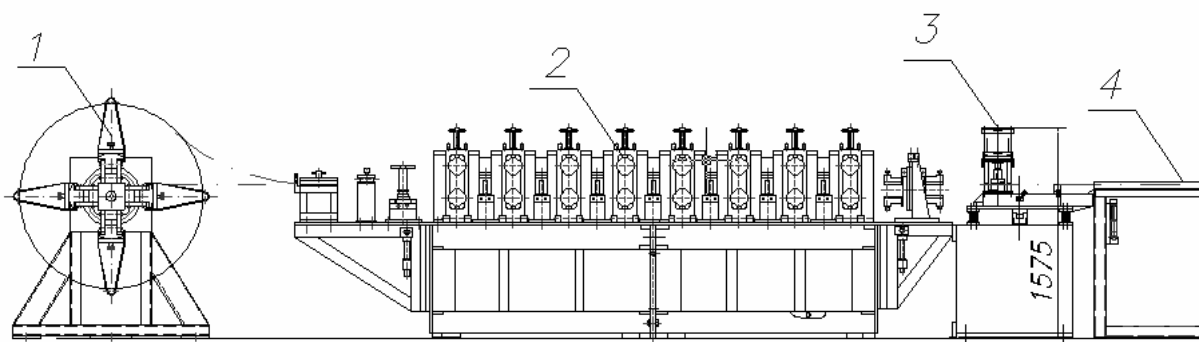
Автоматическая линия на базе станка СПУ-400К8х65: 1 – рулонница; 2 – станок СПУ; 3 – отрезной пневматический пресс; 4 – стол приемный
